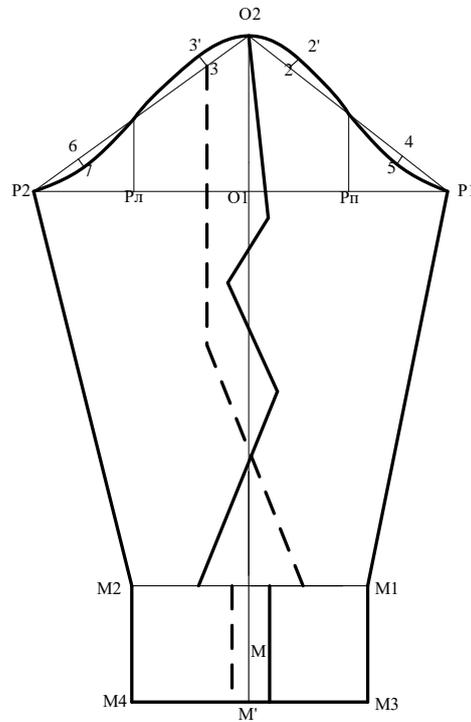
Чертеж модельной конструкция рукава блузки (164-84-94)
